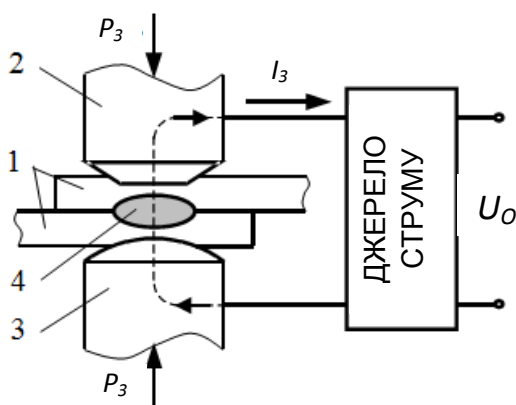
Схема контактної точкової зварювання: 1 – зварні деталі; 2, 3 – електрод; 4 – ядро
